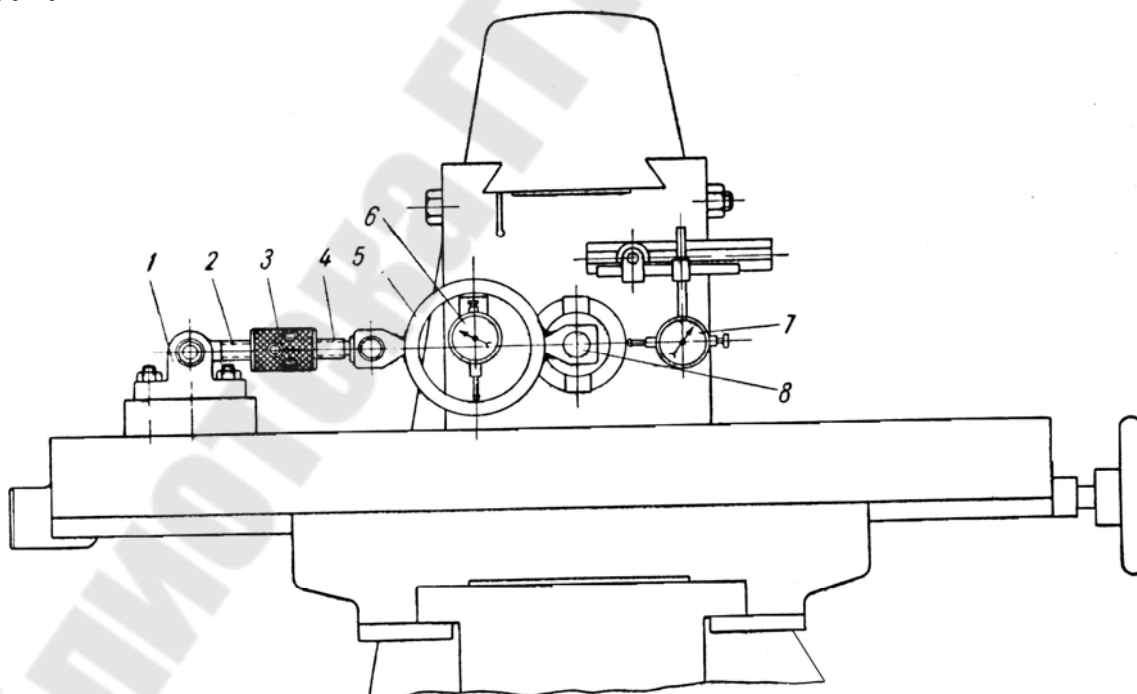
Схема измерения жесткости шпиндельного узла фрезерного станка
